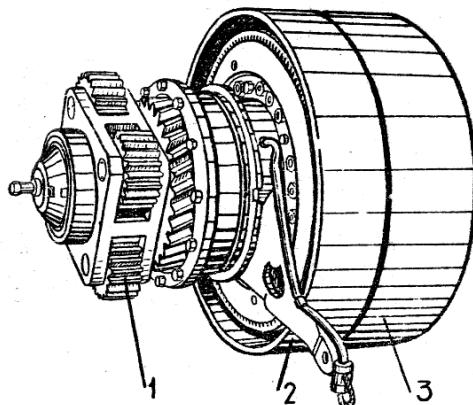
Механізм повороту (загальний вигляд):
